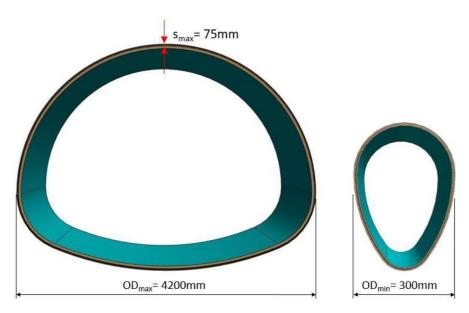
Dimensiones máximas y mínimas de tubería PRFV NC
